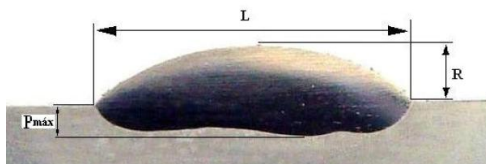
Dimensões geométricas dos cordões de solda abordadas no presente trabalho
